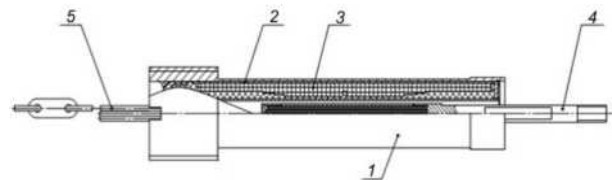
Конструктивная схема датчика: 1 – корпус; 2 – магнитопровод; 3 – катушка; 4 – подвижная часть; 5 – выводы
